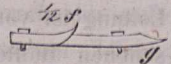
ein senkrechter Durchschnitt, Fig. 319 die Ansicht von unten, Fig. 320 bloß die Ansicht des Bohrgehäuses von oben, Fig. 321 die Ansicht der inneren Seite eines Sägeblattes, Fig. 322 die untere Ansicht desselben, Fig. 323 die Seitenansicht des Doppelmessers und endlich Fig. 324 die untere Ansicht desselben, wovon die letzten 4 Figuren nach einem doppelt so grossen Massstabe gezeichnet sind, als die ersten vier, welche in dem Verhältnisse wie 1 : 24 dargestellt erscheinen.
